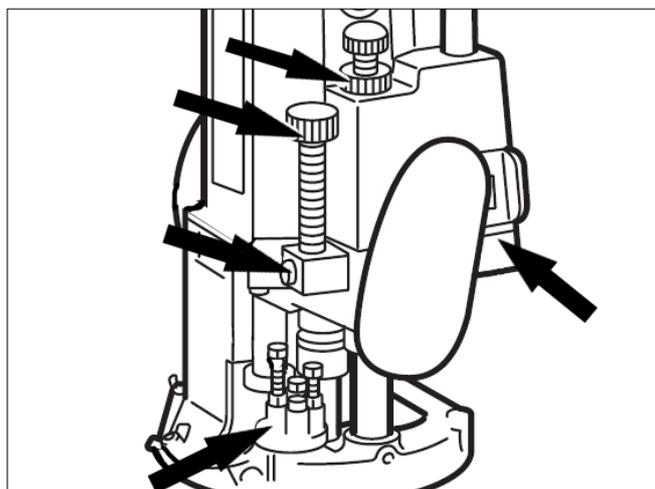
Регулировка глубины фрезерования ФМ-1900Э
